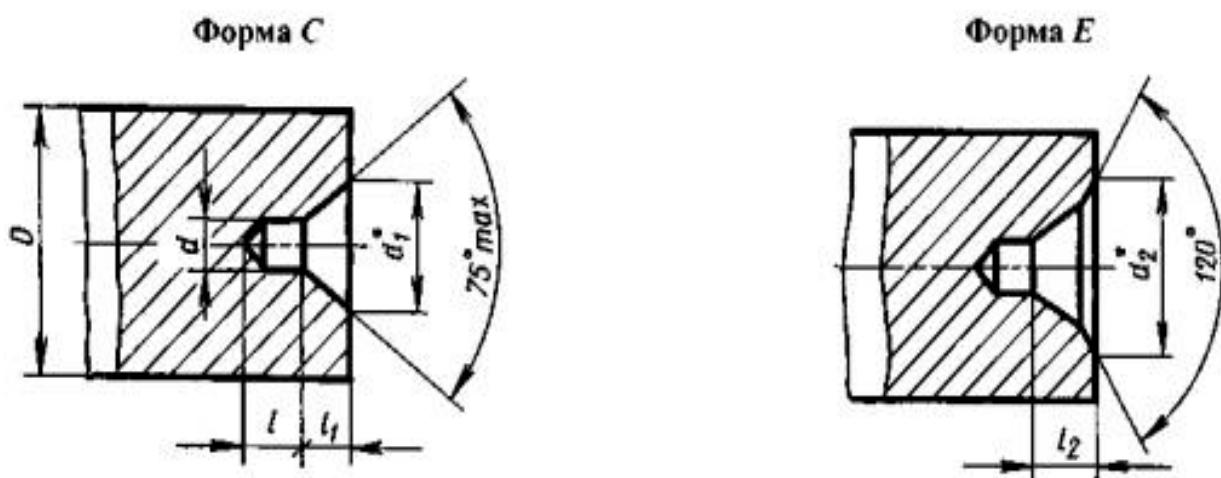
Указание форм центровых отверстий на чертеже детали
